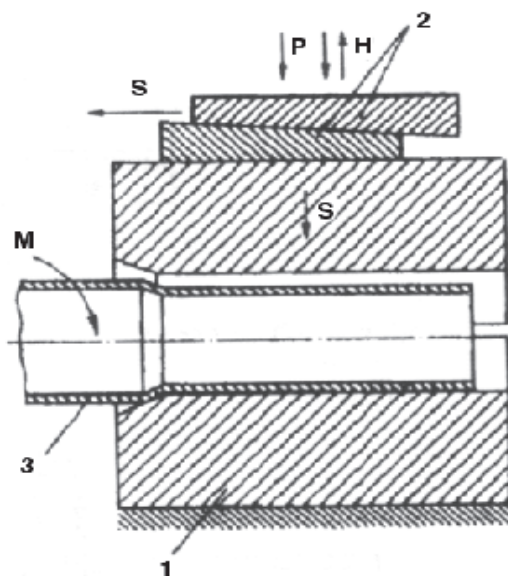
Схема калибровки патрубков по всей длине с постепенным изменением закрытой высоты штампа:
